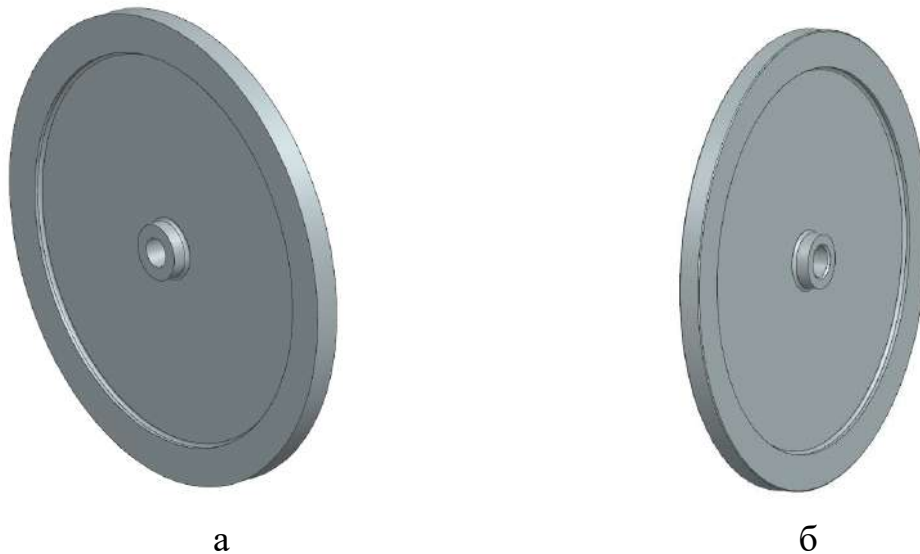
3D зображення деталі після обробки (а) та до обробки (б)
